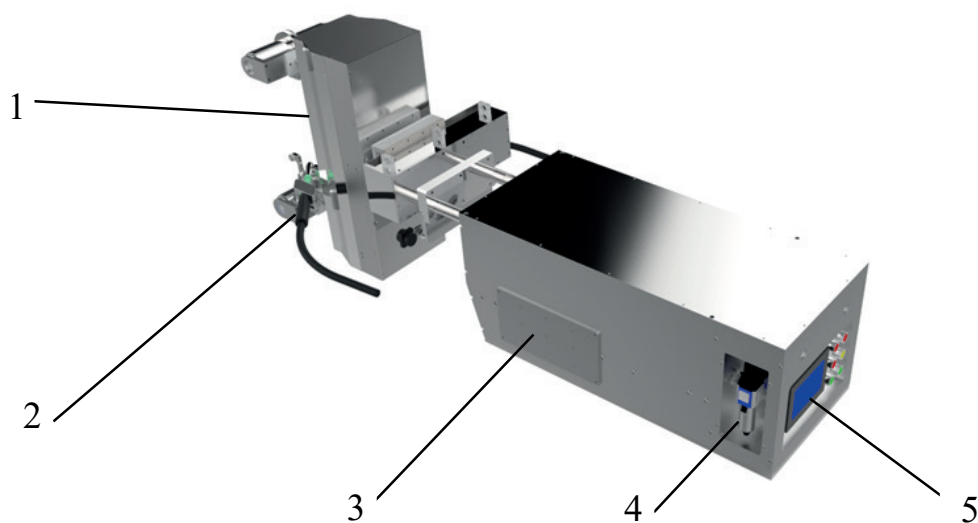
а – Схема устройства автоматического сварочного робота: 1 – сварочная головка, 2 – сварочная горелка, 3 – смотровое окно, 4 – манометр, 5 – панель управления
